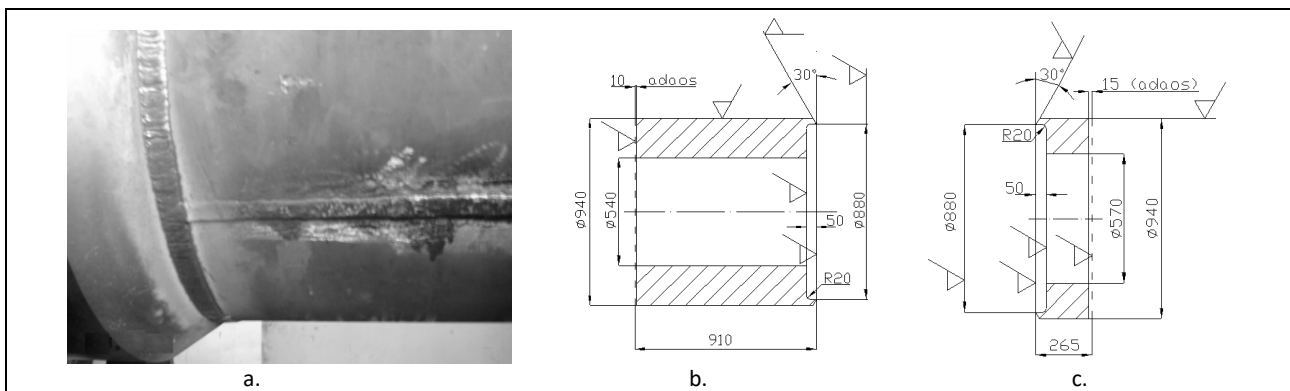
Componentele de etanșare ale tubului etambou (a. virolă sudată, b. bucsă pupa, c. bucsă prova)
